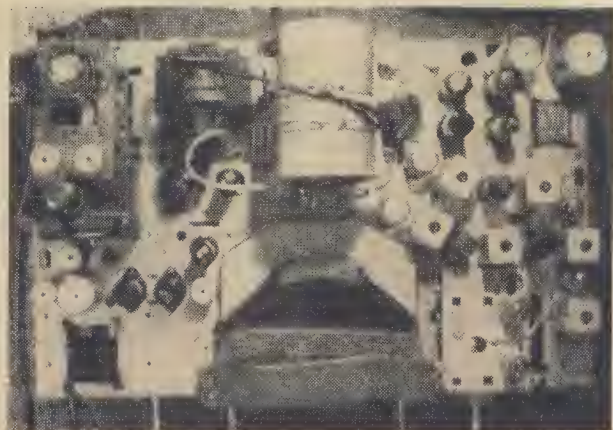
Aufsicht auf das Chassis ohne Bildröhre. Lage der Teile vgl. mit Bild 6
